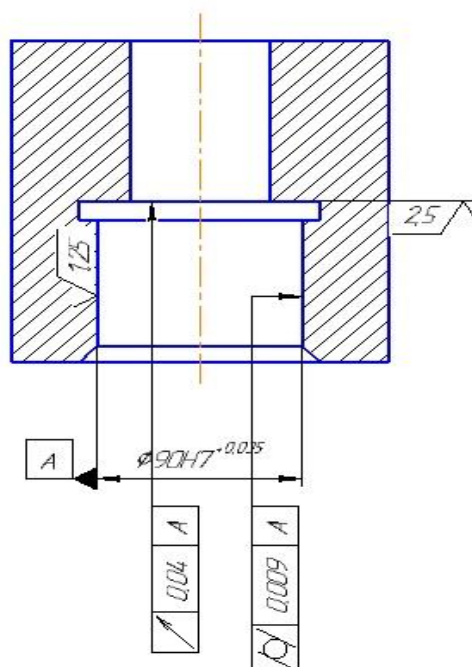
Изображение поля допуска подшипника для вала
